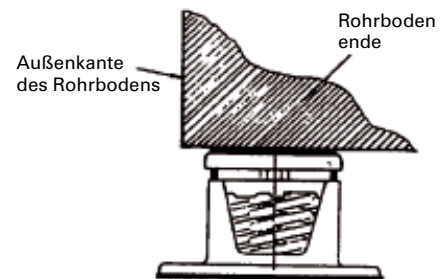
Ausrichtung Maschinenstandfuß/Federdämpfer
